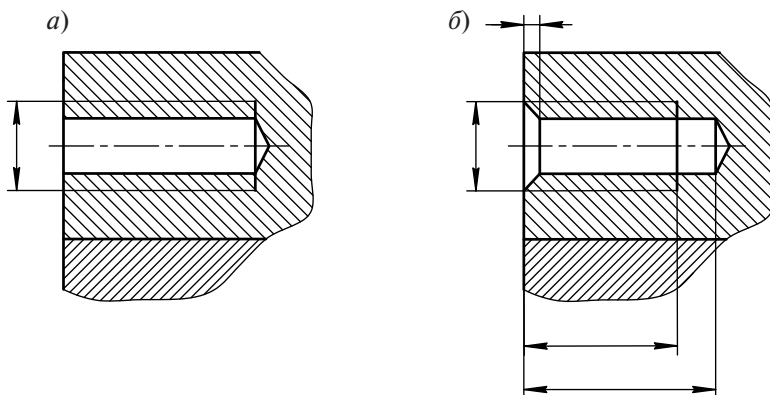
Изображение глухого отверстия на чертеже общего вида и чертеже детали
